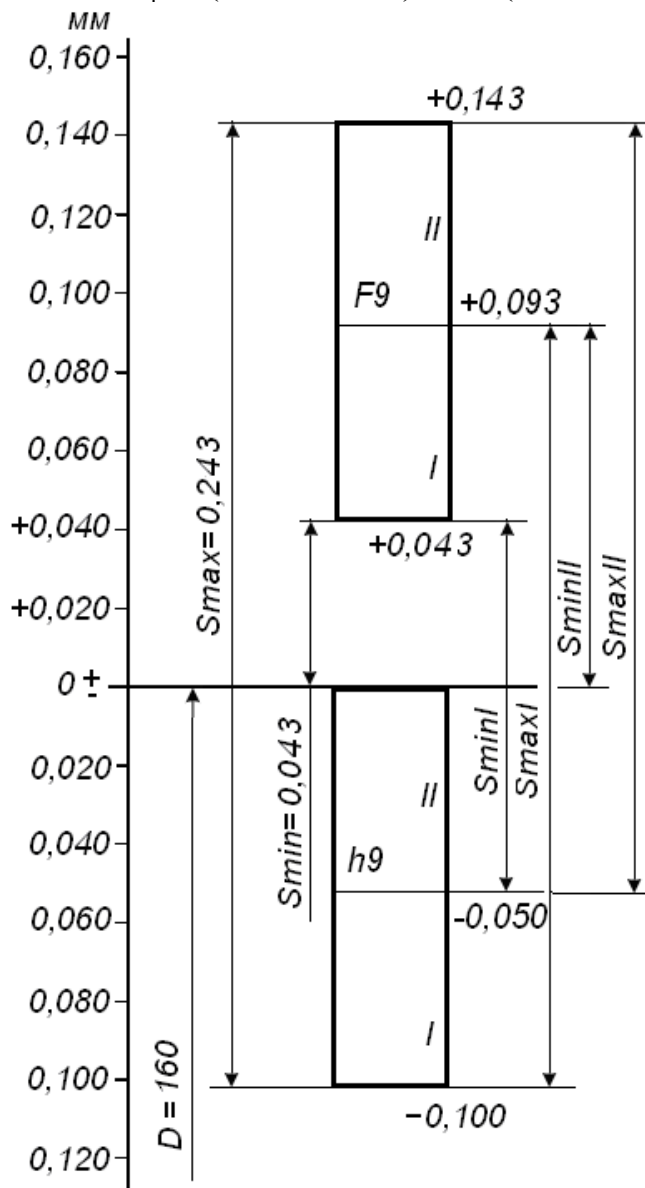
Схема розташування полів допусків з'єднання Ø160F9/h9
